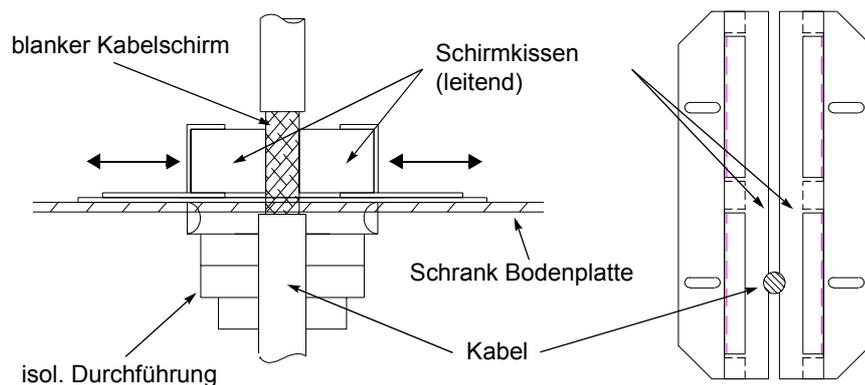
Beispiel für 360°-Erdung einer Steuerkabeldurchführung (Seitenansicht und Draufsicht).
